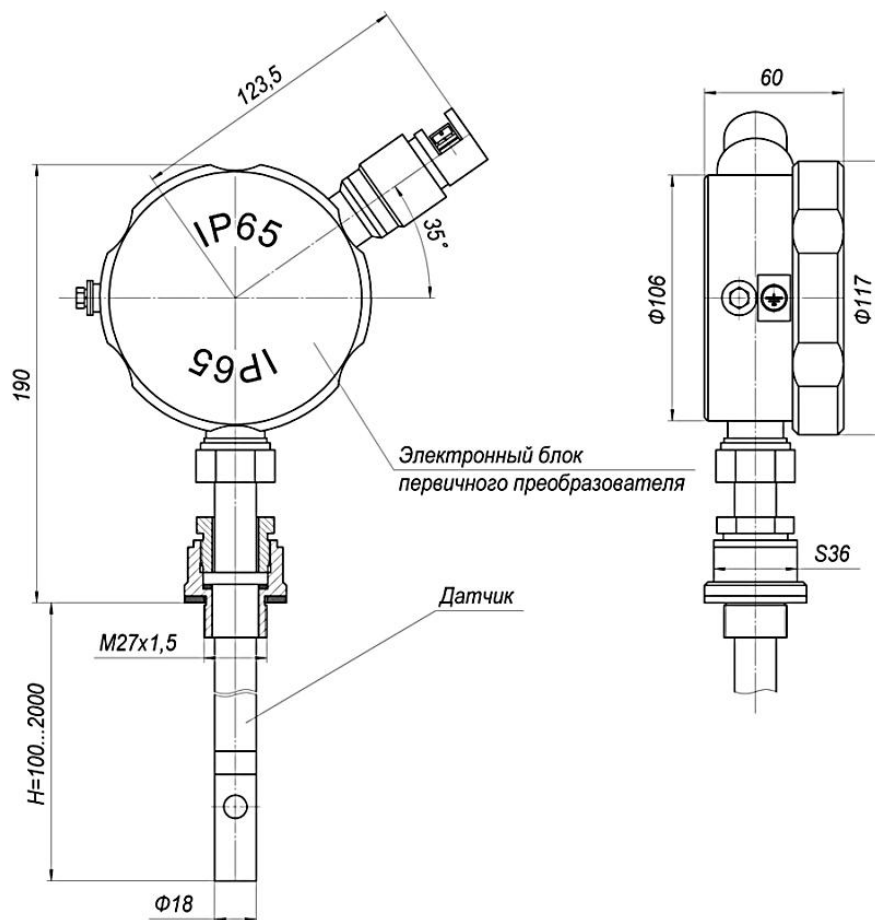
Габаритные, установочные и присоединительные размеры моноблочного первичного преобразователя погружного типа, тип корпуса ПП - "Н" (нерж. сталь)
